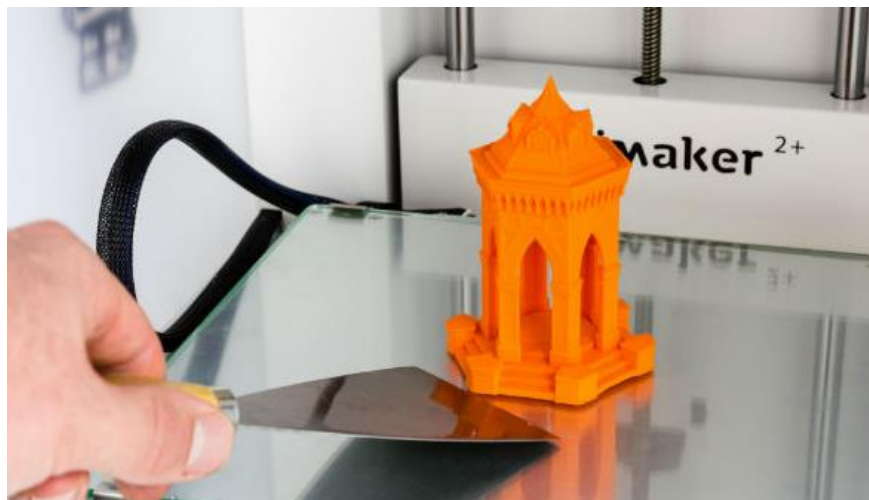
Extracción de una pieza en una máquina de impresión 3D de MDF. Fuente: <https://lacountylibrary.org/removing-3d-prints/>
